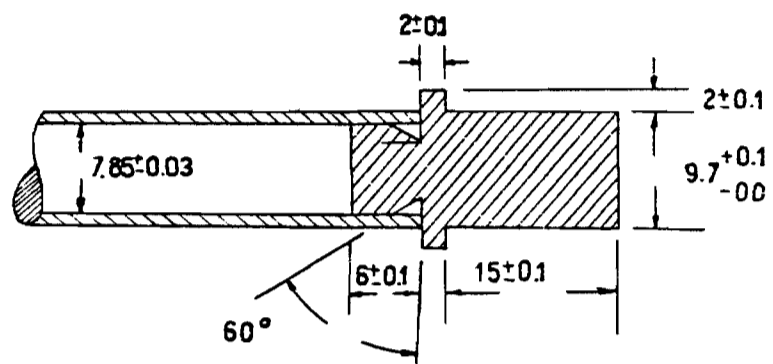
Diseño de junta utilizado para el elemento combustible RA-1, 2a. carga.
